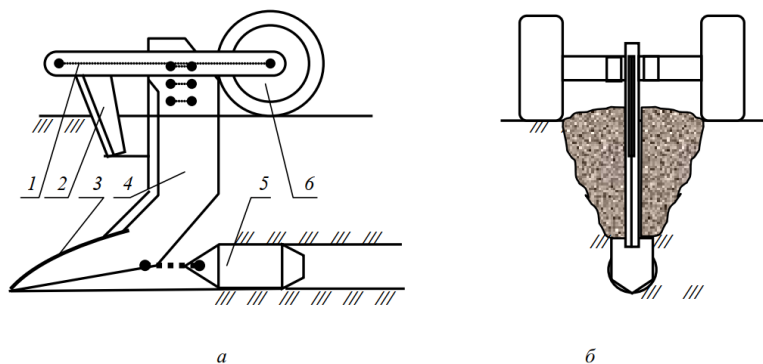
Рыхлитель-котователь: а – вид сбоку; б – вид спереди: 1 – рама; 2 – дернорез; 3 – пластина; 4 – основной нож; 5 – дренир; 6 – опорные колеса
